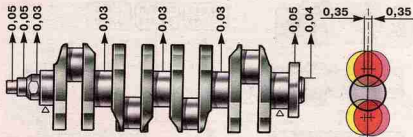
Допустимые биения основных поверхностей коленчатого вала
